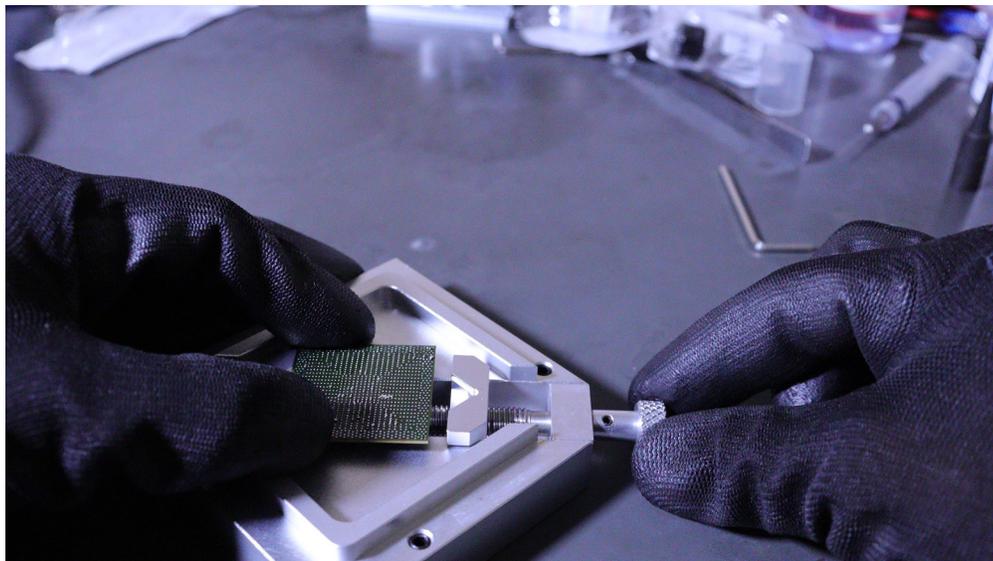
posicionando o chip no Suporte BGA Honton Ht 90x90
